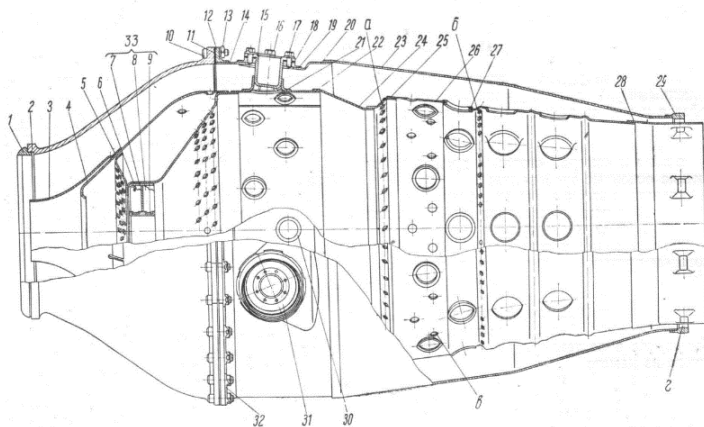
Конструкция трубчатой камеры сгорания двигателя ВК-1:
